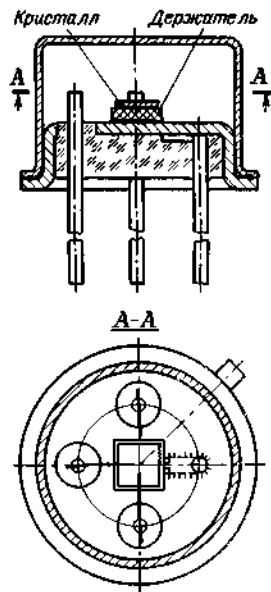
Конструкция корпуса КТ-22. Вариант для монтажа кристалла на керамический держатель.
